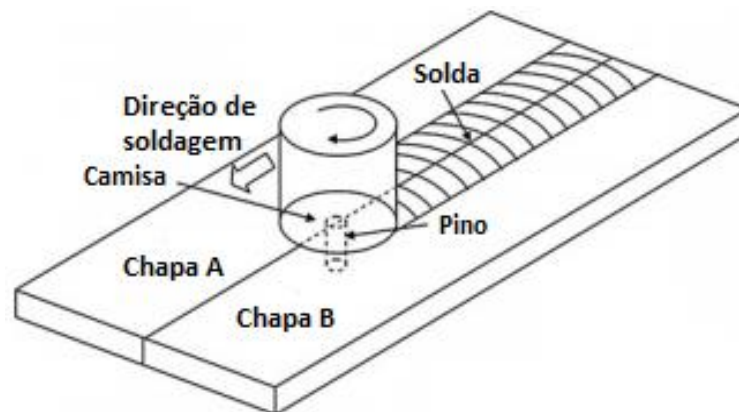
Ferramenta para soldagem FSW composta por pino e camisa indicando a direção de soldagem (NANDAN 2008).
